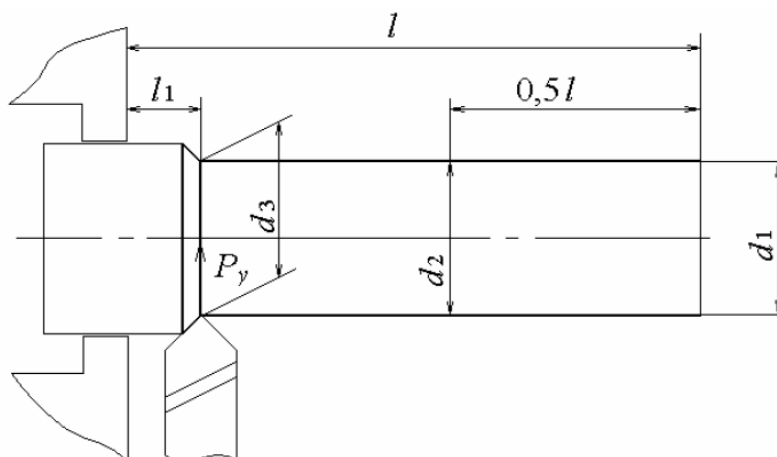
Схема замера диаметров и размеров длин обработанной заготовки
